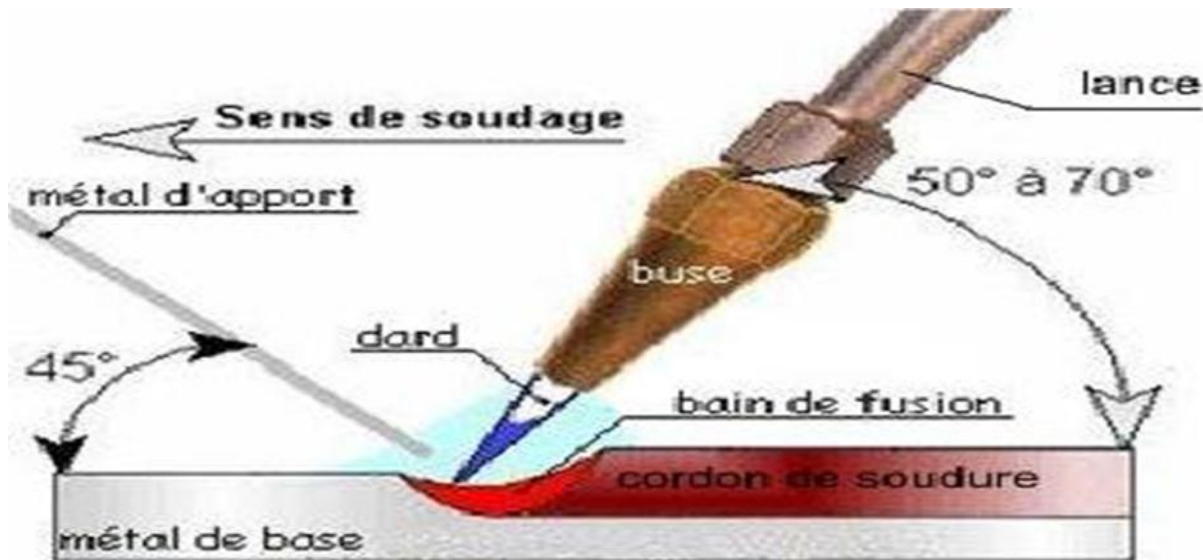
Soudage oxyacétylénique [7].
